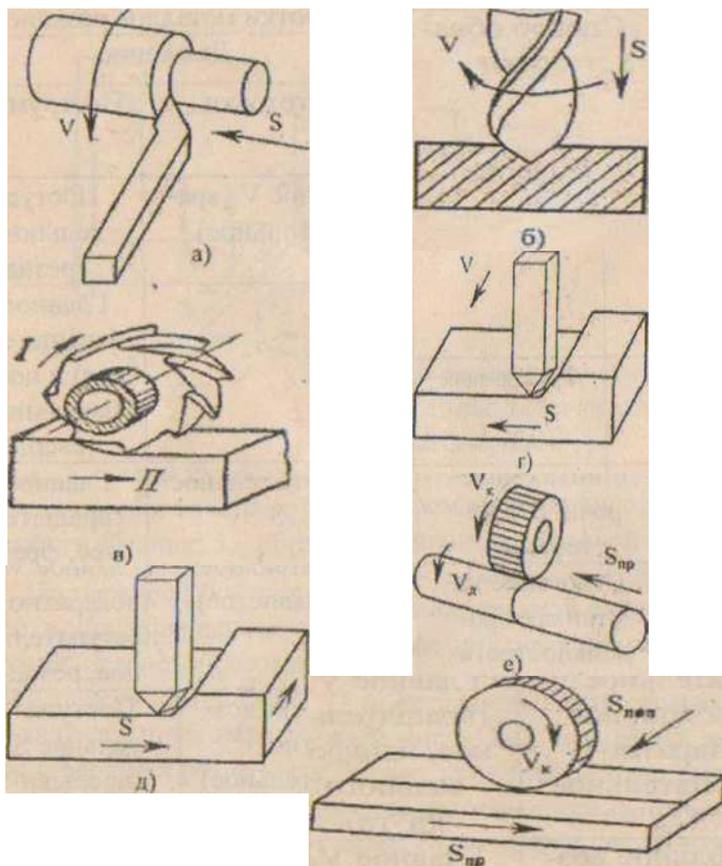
Основные способы обработки металлов: а – точение; б – сверление; в – фрезерование; строгание на станках поперечного- (г) и продольнострогательных (д); шлифование наружное, круглое(е) и плоское (ж)
